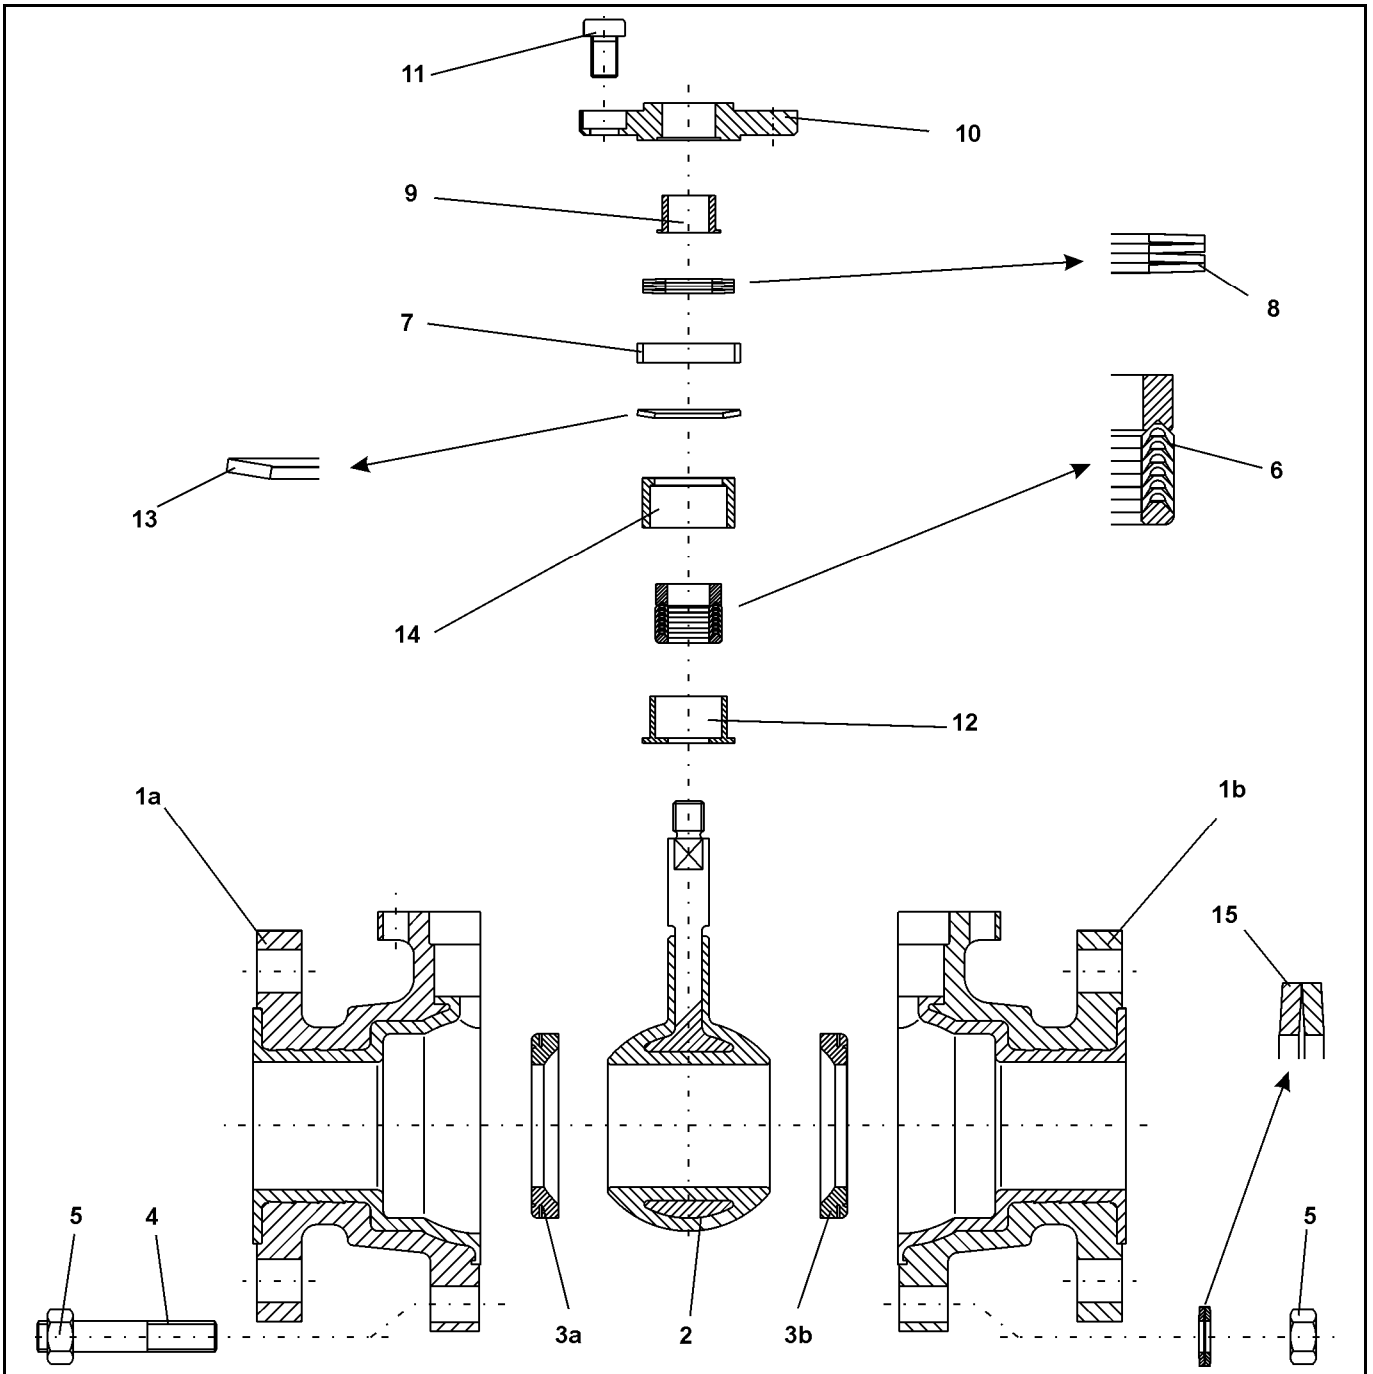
Explosionszeichnung des ANSI-Kugelhahns BR 20a
